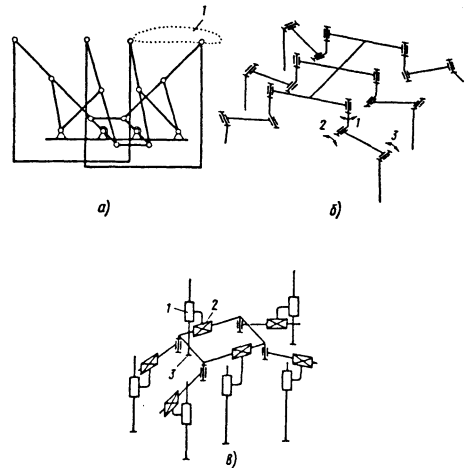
Примеры шагающих движителей: а - стопоходящая машина конструкции П. Л. Чебышева; б - инсектоморфный движитель; в - ортогональный движитель
